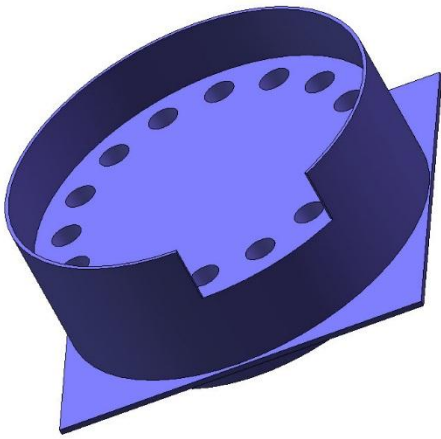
Інструментальний магазин оброблювального центра VA 500.
